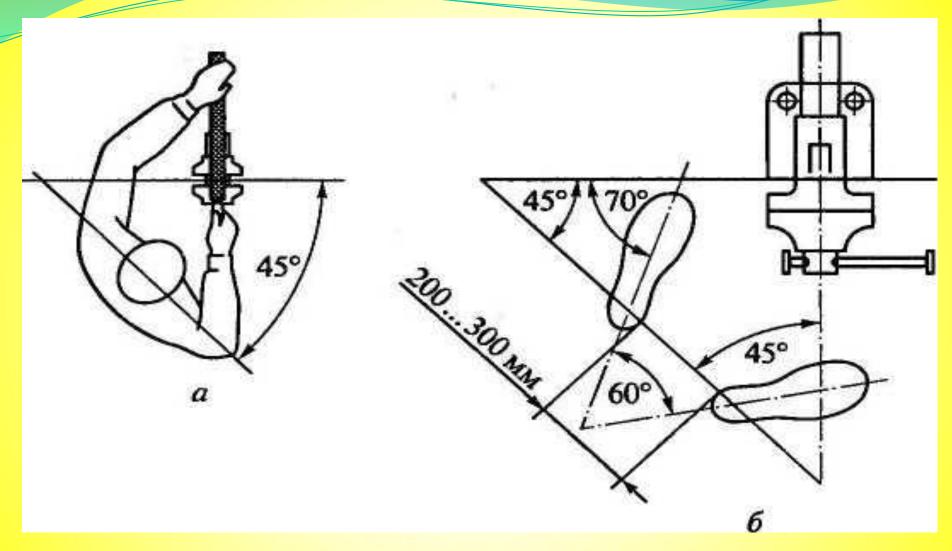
Положение рабочего: а — положение рук и корпуса; б - положение ног
